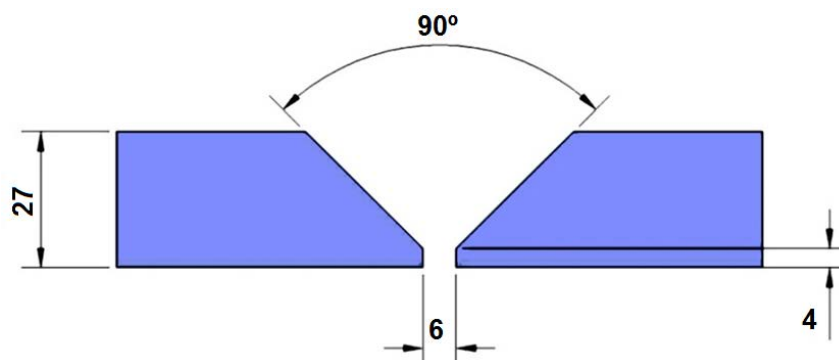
Dimensões da peça de teste preparada para a execução de soldagem.
